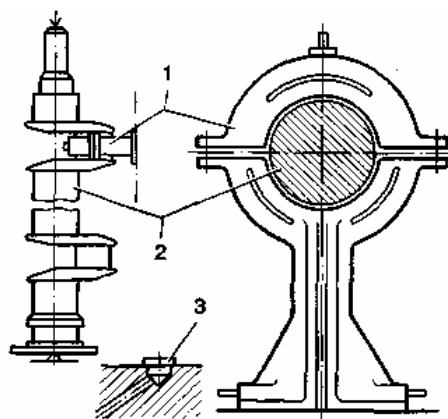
Приспособление для контроля размеров шеек коленчатого вала
